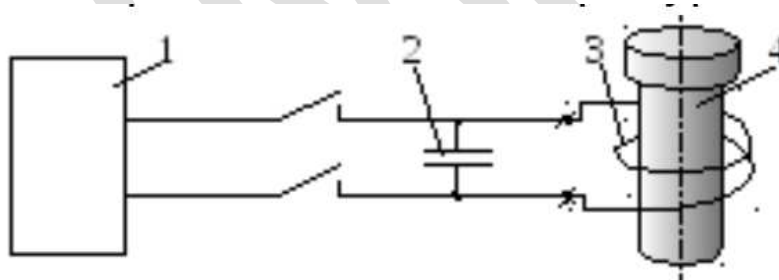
Схема нагріву деталі СВЧ: 1 - генератор струму високої частоти; 2 - конденсатор; 3 - індуктор; 4 – деталь [8]
